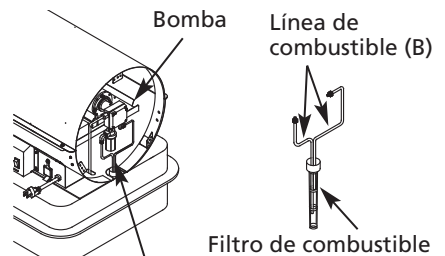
Desmontaje del Filtro de Combustible del Tanque
